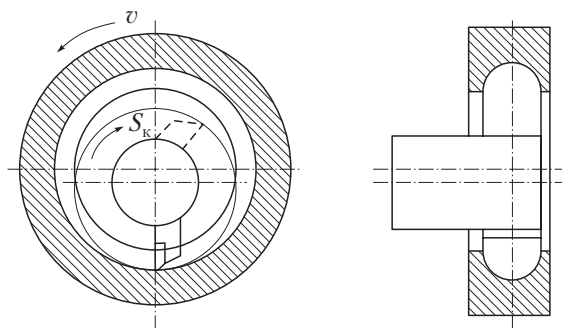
Схема процесса обработки беговых дорожек на кольцах подшипников
